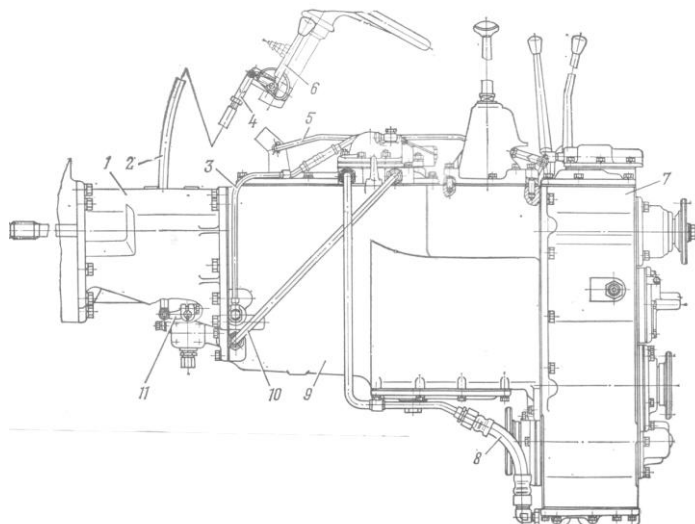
Загальний вигляд коробки передач з роздавальною коробкою: 1 - проставочний корпус; 2 тяга; 3 і 10 - трубки; 4 - регулювальна вилка; 5 - тяга блокування; 6 - важіль перемикання передач; 7 - роздавальна коробка; 8 - шланг; 9 - коробка передач; 11 - важіль перемикання передач.
